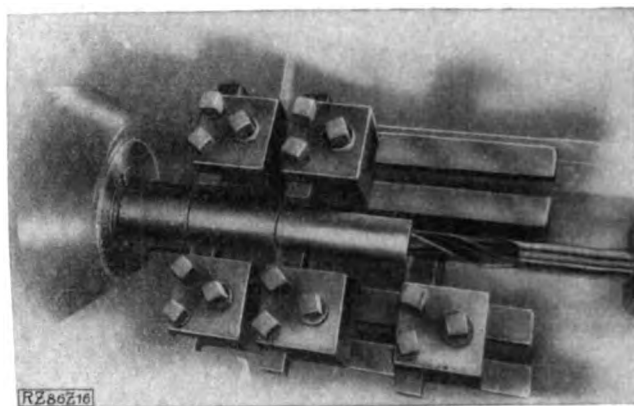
Vollständig unterstützter Werkzeughalter für sechs Werkzeughalter. Werkzeuge von Hasse & Wrede.
